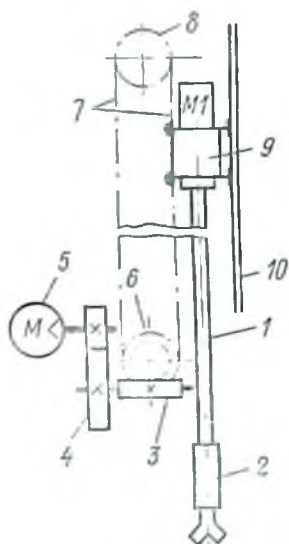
Кинематическая схема вращательно-подающего механизма с цепной подачей бурового станка СБУ-125-24
